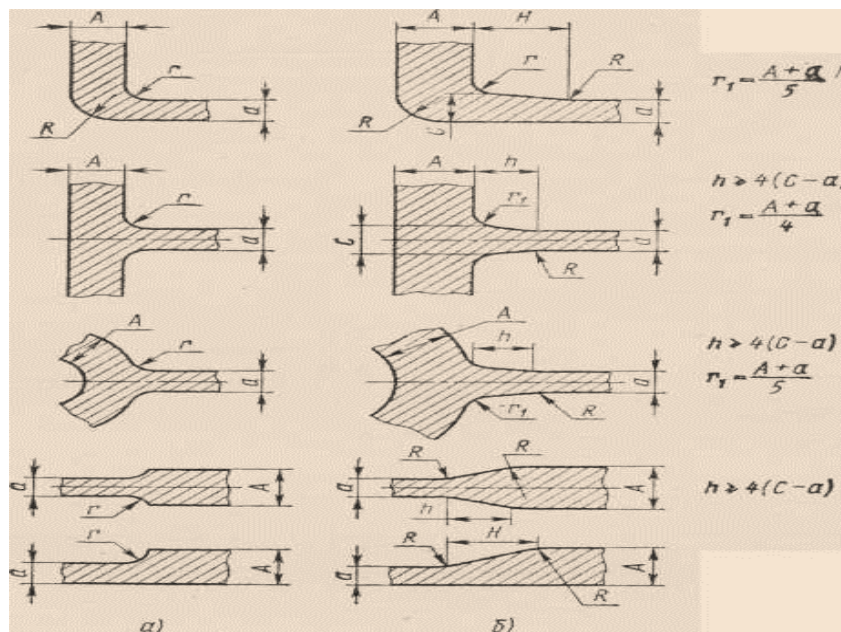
Рекомендуемые переходы от стенки к стенке в литых деталях:
